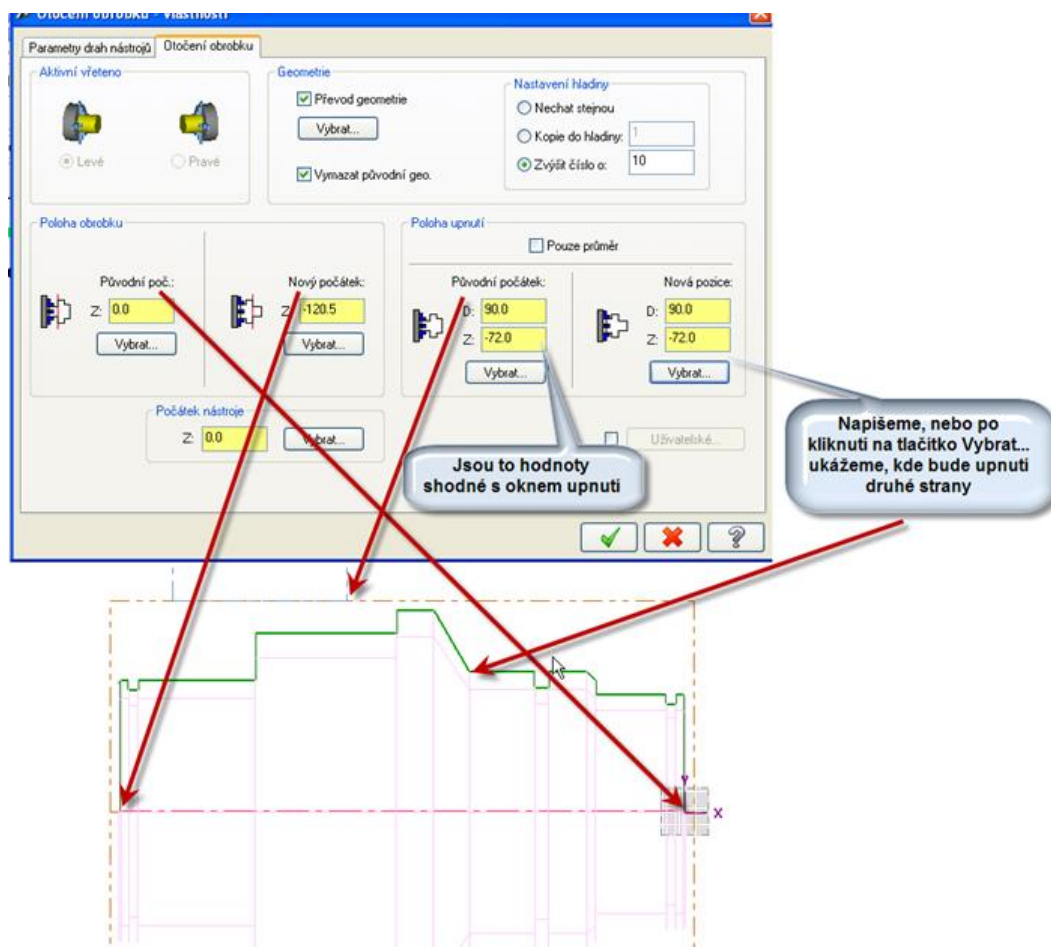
Výběr geometrie při otočení obrobku pomocí příkazu Dráhy nástrojů/Různé/Otočit obrobek
